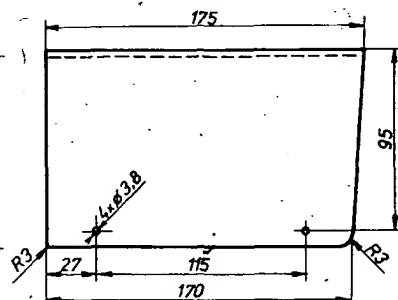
Zadní panel - Al polotvrdý - 1 ks
